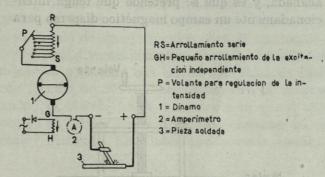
Esquema de una dinamo de soldadura A. E. G.
